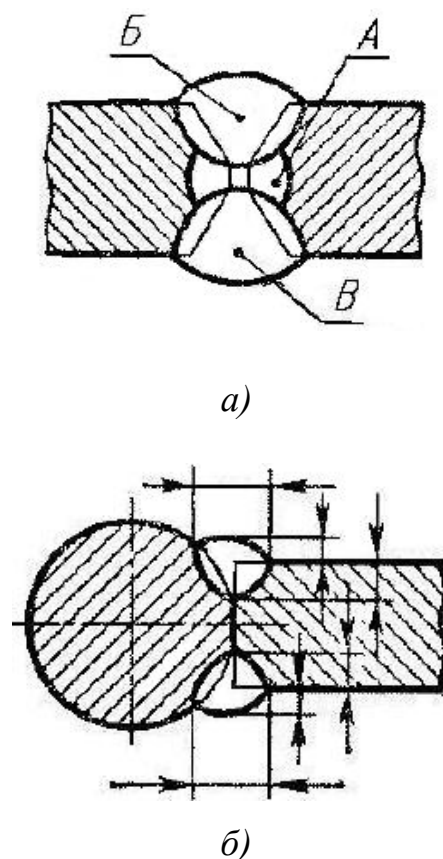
Виды сварных соединений: а) многопроходной шов; б) нестандартный шов
